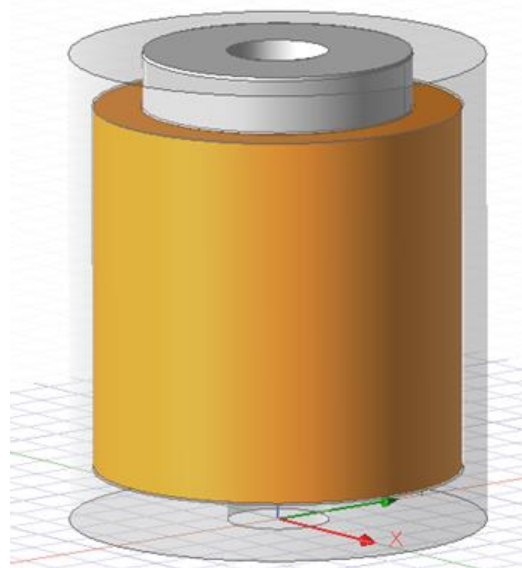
Загальний вигляд електромеханічного амортизатора
